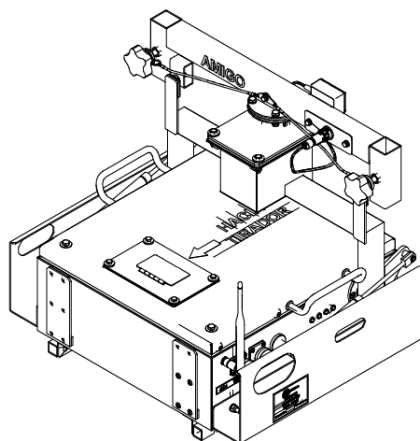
Vista general de blanco fijo. Fuente: CENAD de San Gregorio.
